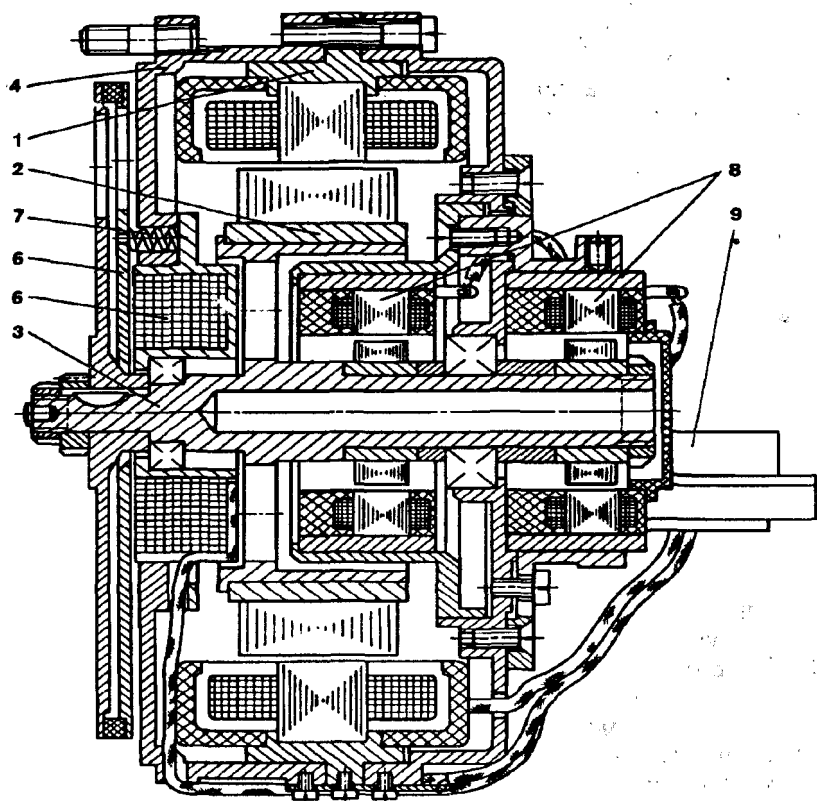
Конструктивная схема резервированного привода мотор-колеса на базе электродвигателя ДБМ-100:
